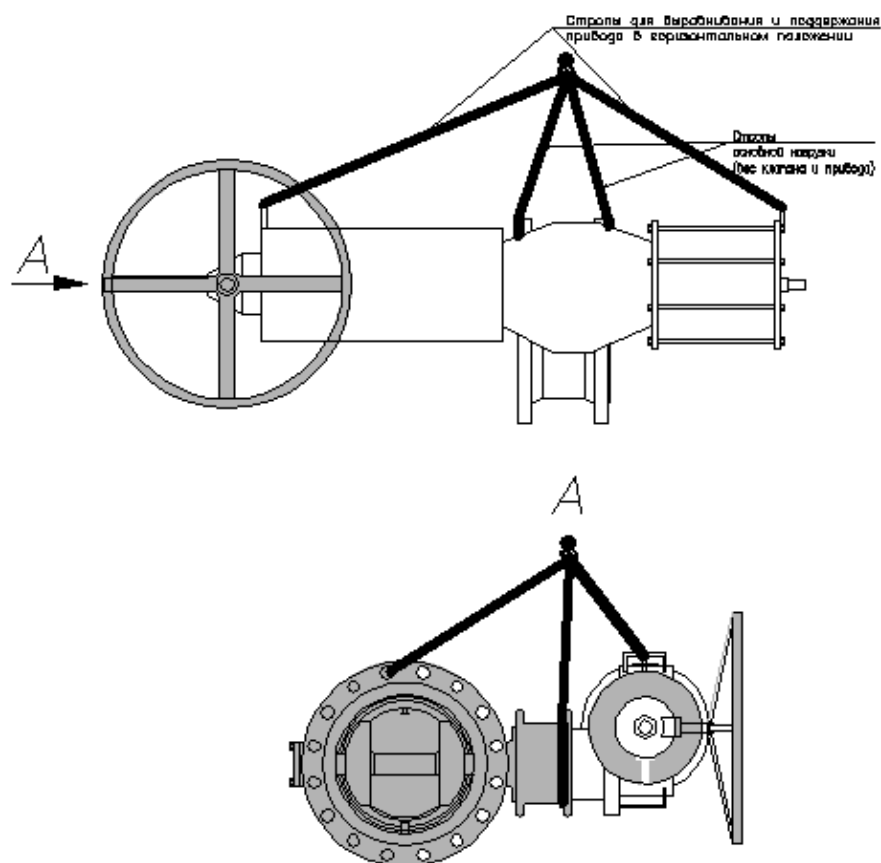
Схема строповки затвора дискового с горизонтальной ориентацией вала.
